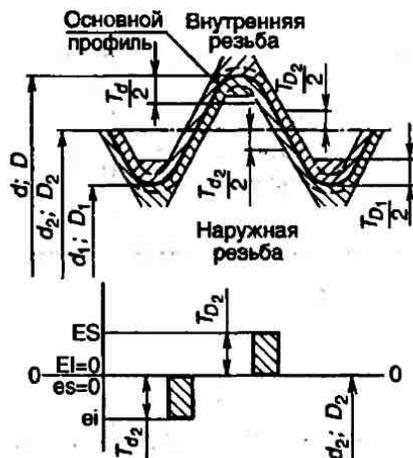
Положения полей допусков трубной цилиндрической резьбы:
